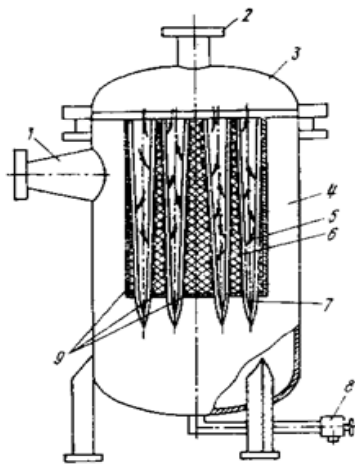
Конструкція фільтра–сепаратора СТ–500–2: 1–вихідний патрубок; 2–патрубок входу; 3–кришка; 4–корпус; 5–фільтрувальний чохол; 6–водовіддільний чохол; 7–шлейфи; 8–патрубок зливу; 9–каркас
